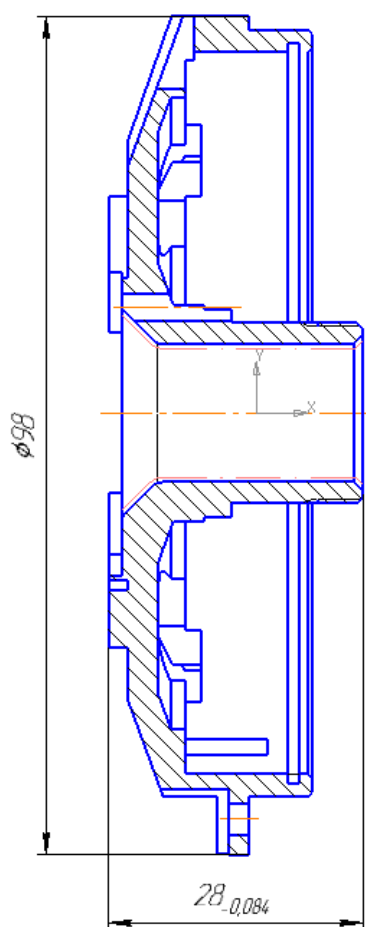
2D модель детали "Корпус опоры 2"
